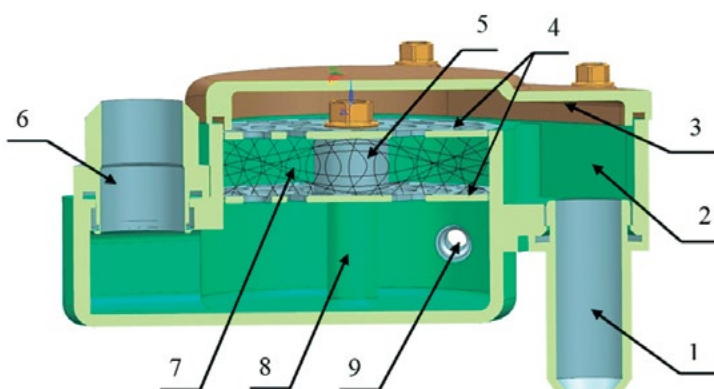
Основные элементы опытного маслоотделителя: 1 — патрубок для приёма газомасляной смеси; 2 — корпус; 3 — крышка корпуса маслоотделителя; 4 — перегородки; 5 — проставка; 6 — патрубок для выпуска отсепарированных картерных газов; 7 — маслоосадительная сетка; 8 — центральный осевой элемент в корпусе маслоотделителя; 9 — сливной патрубок для слива осаждённого масла
